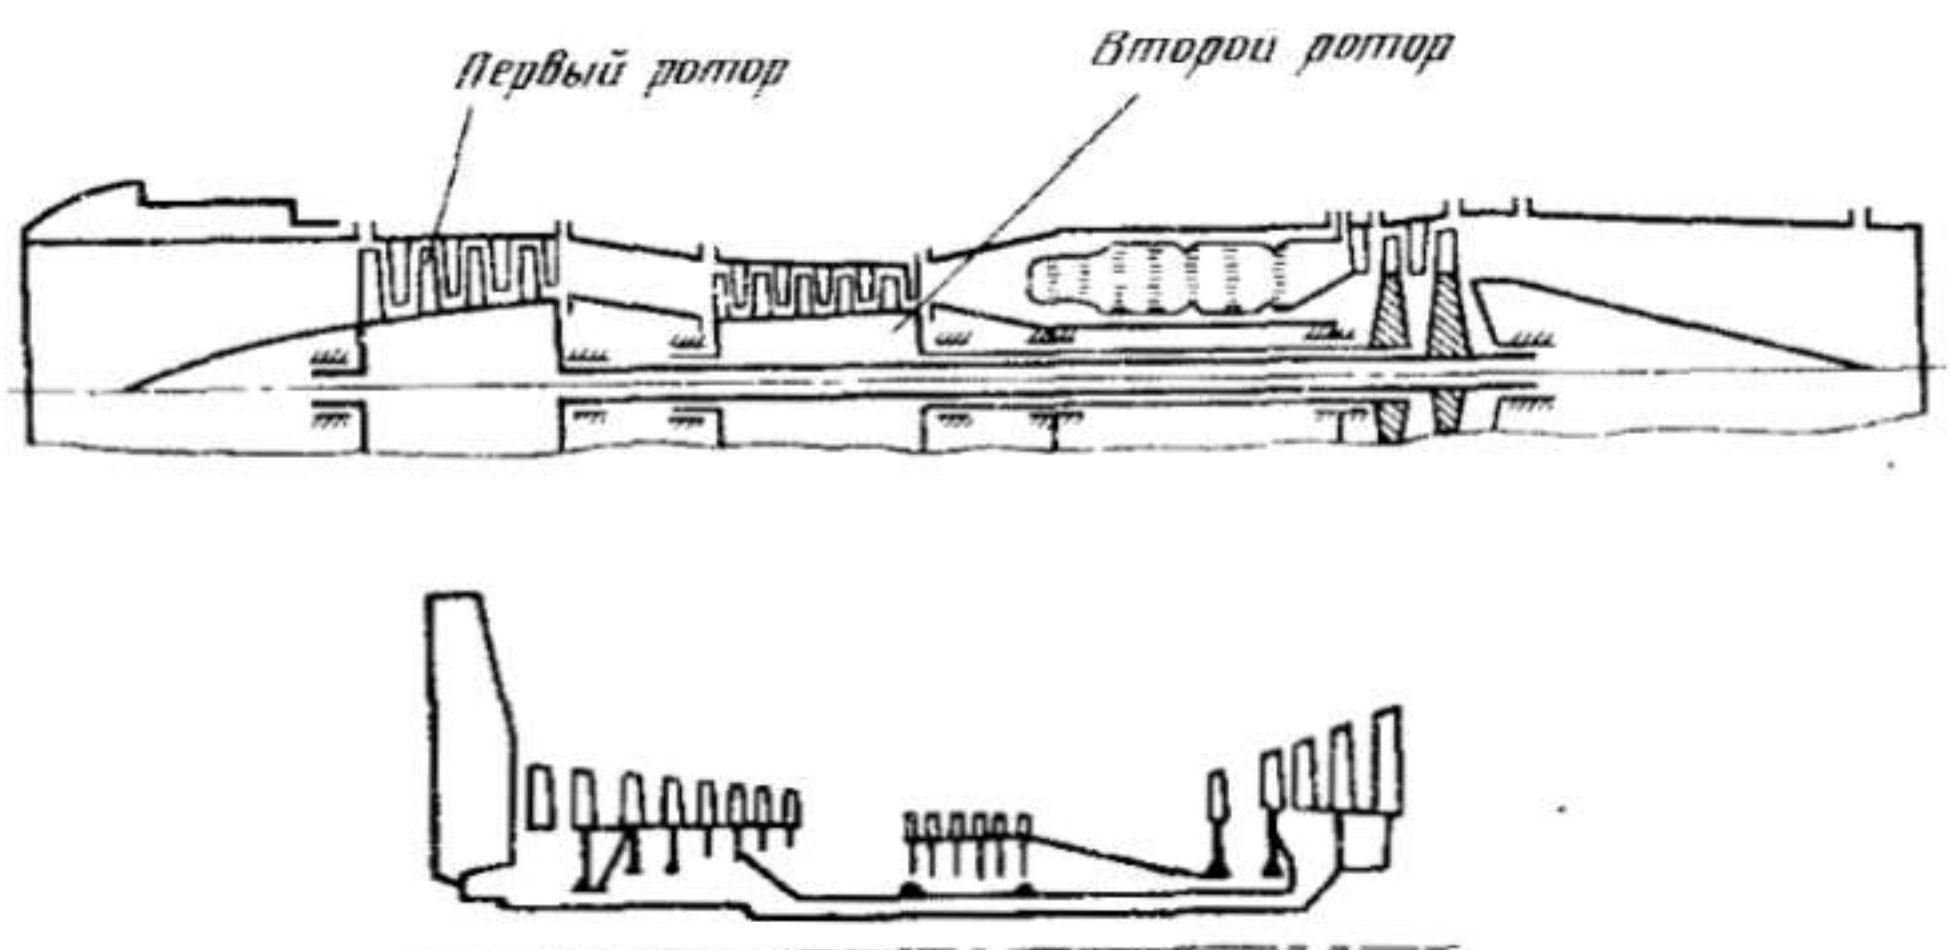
Двухкаскадний компресор стандартної схеми
